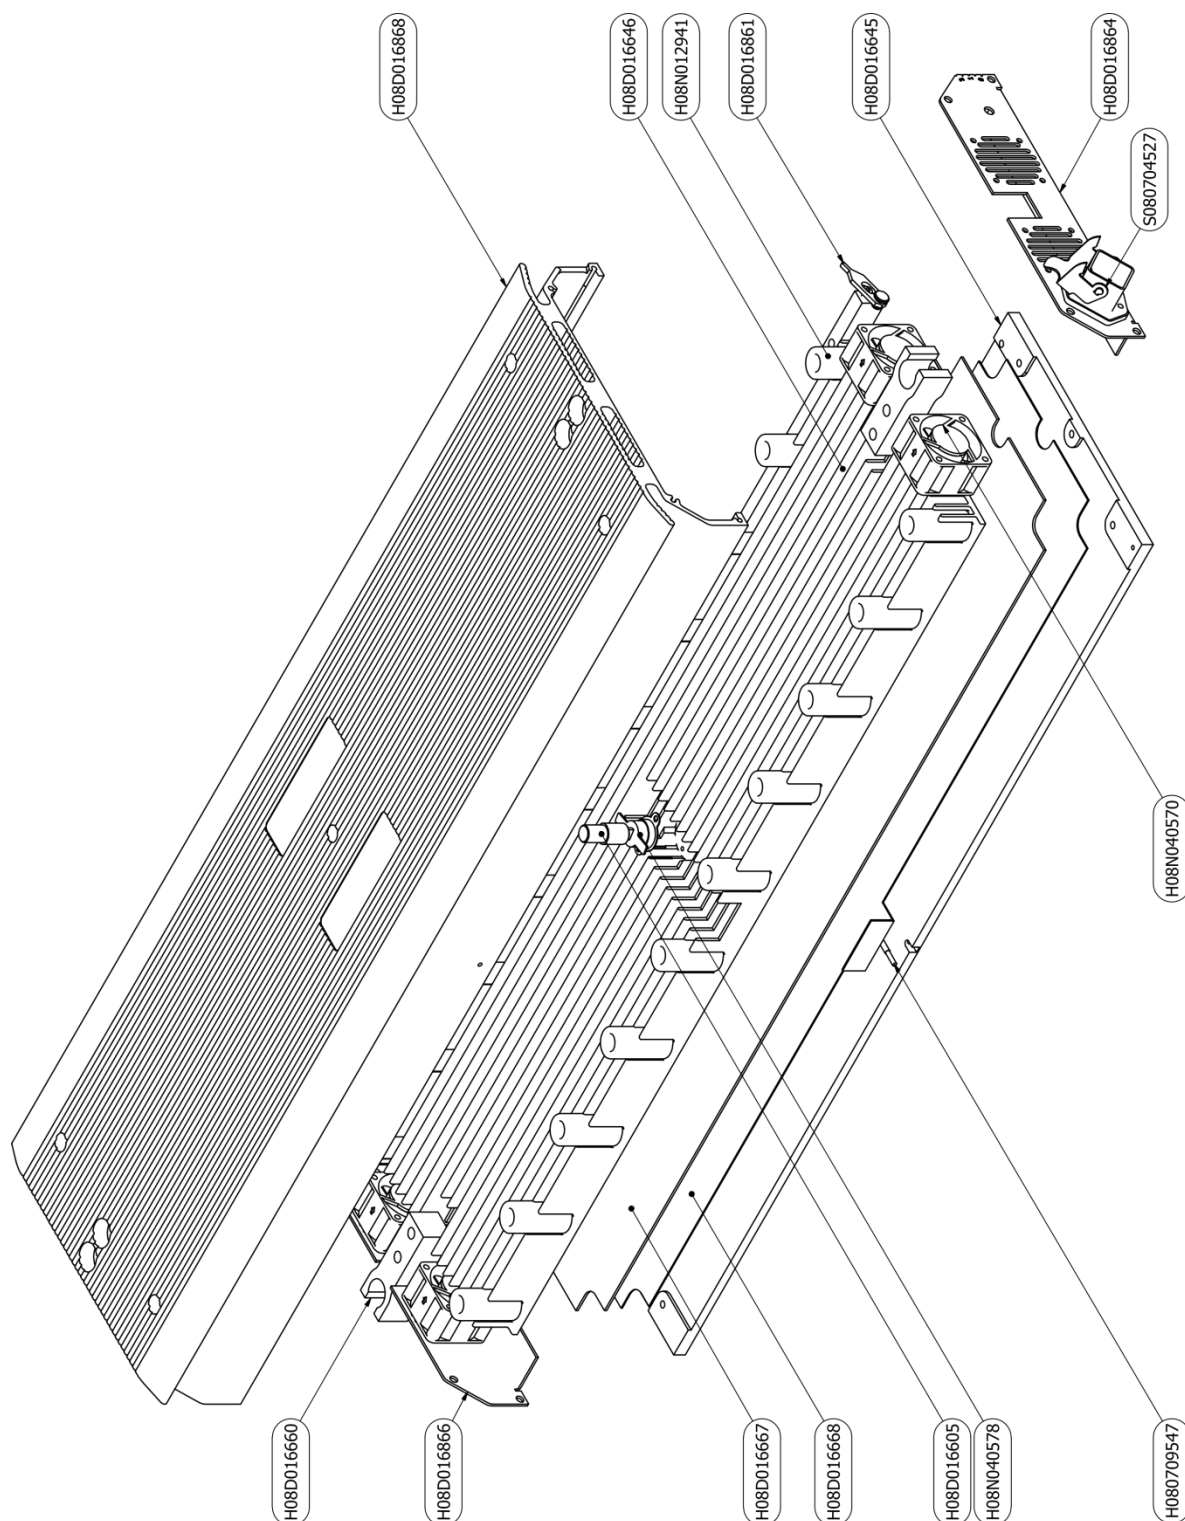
H08D016644 Assemblage de plaque chauffante supérieure PML-600
